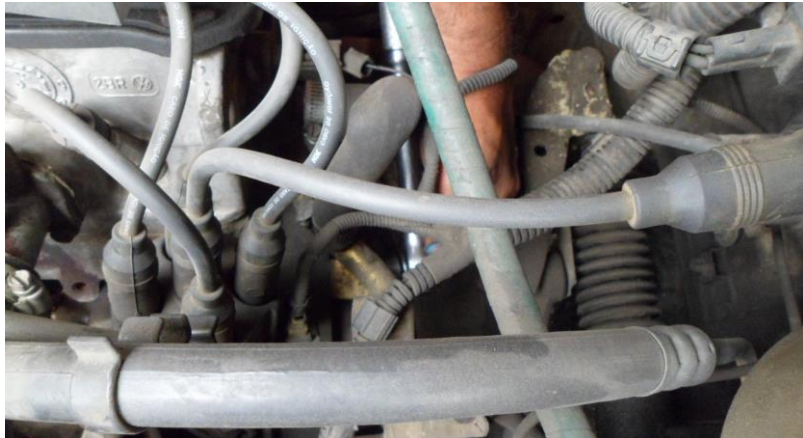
SOLTAR TORNILLOS DE SOPORTE DEL MOTOR
